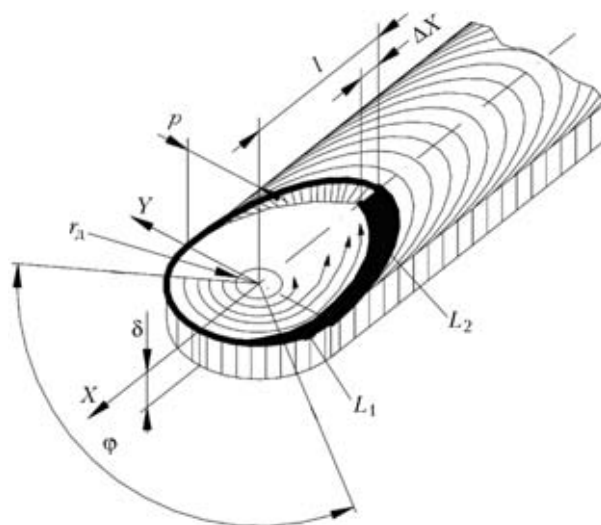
Схема сварочной ванны при сварке с ЭМВ (обозначения см. в тексте)
